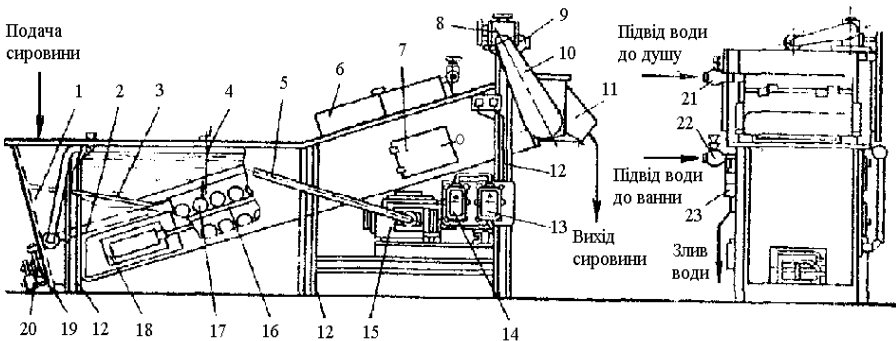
Елеваторна машина КУВ-1: 1 – ванна; 2 – барботер; 3 – решітка; 4 – заслінка; 5 – трубопровід; 6 – душовий пристрій; 7; 19 – люки; 8 – редуктор; 9 – електродвигун; 10 – ланцюгова передача; 11 – вихідний лоток; 12 – стійки; 13; 14 – пускові пристрої; 15 – повітряний компресор; 16 – направляючі; 17 – роликіве полотно; 18 – натяжний пристрій; 20; 23 – вентиля для зливання води; 21; 22 – вентиля для підводу води
